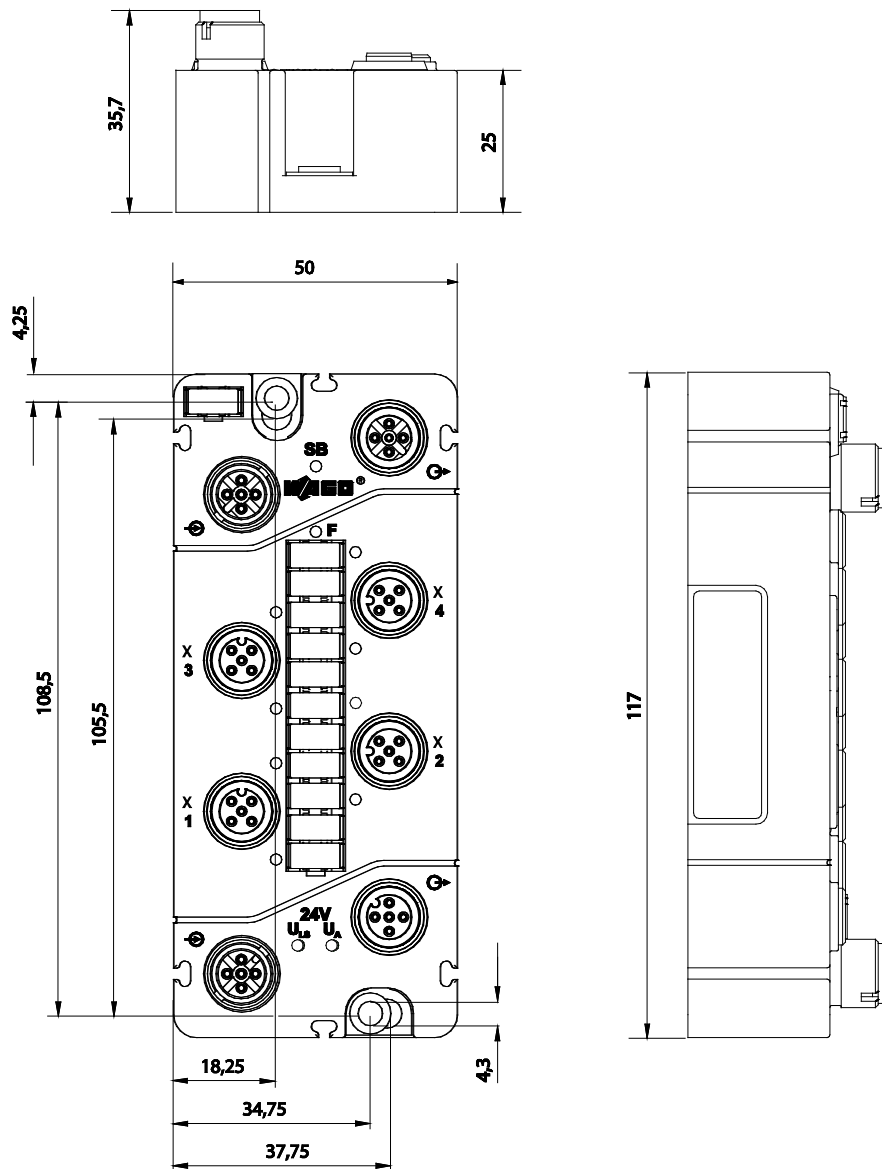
Abmessungen in Millimetern (exemplarisch)
